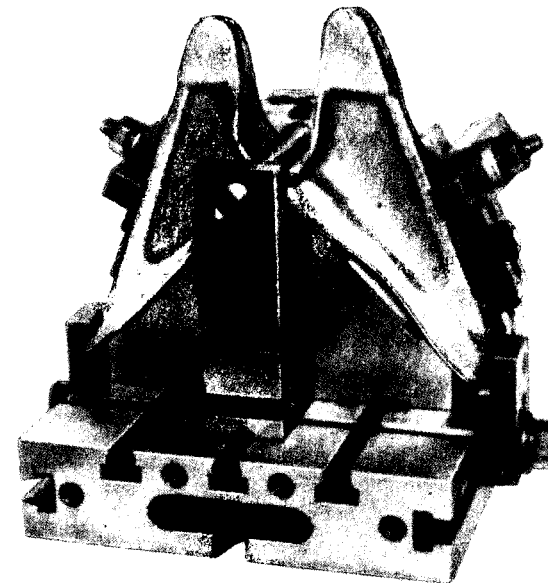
Двухместное приспособление для фрезерования вилки кронштейна
